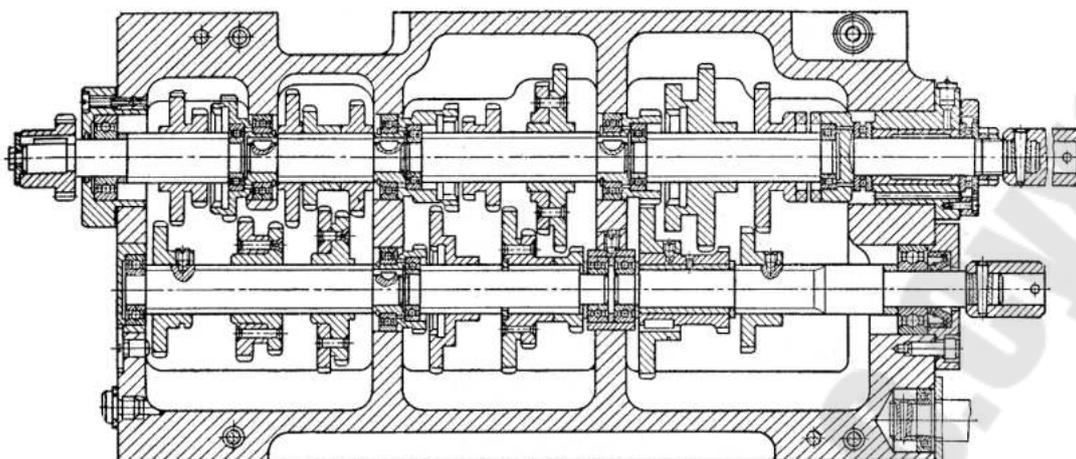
Коробка подач токарно-винторезного станка 1И611П
